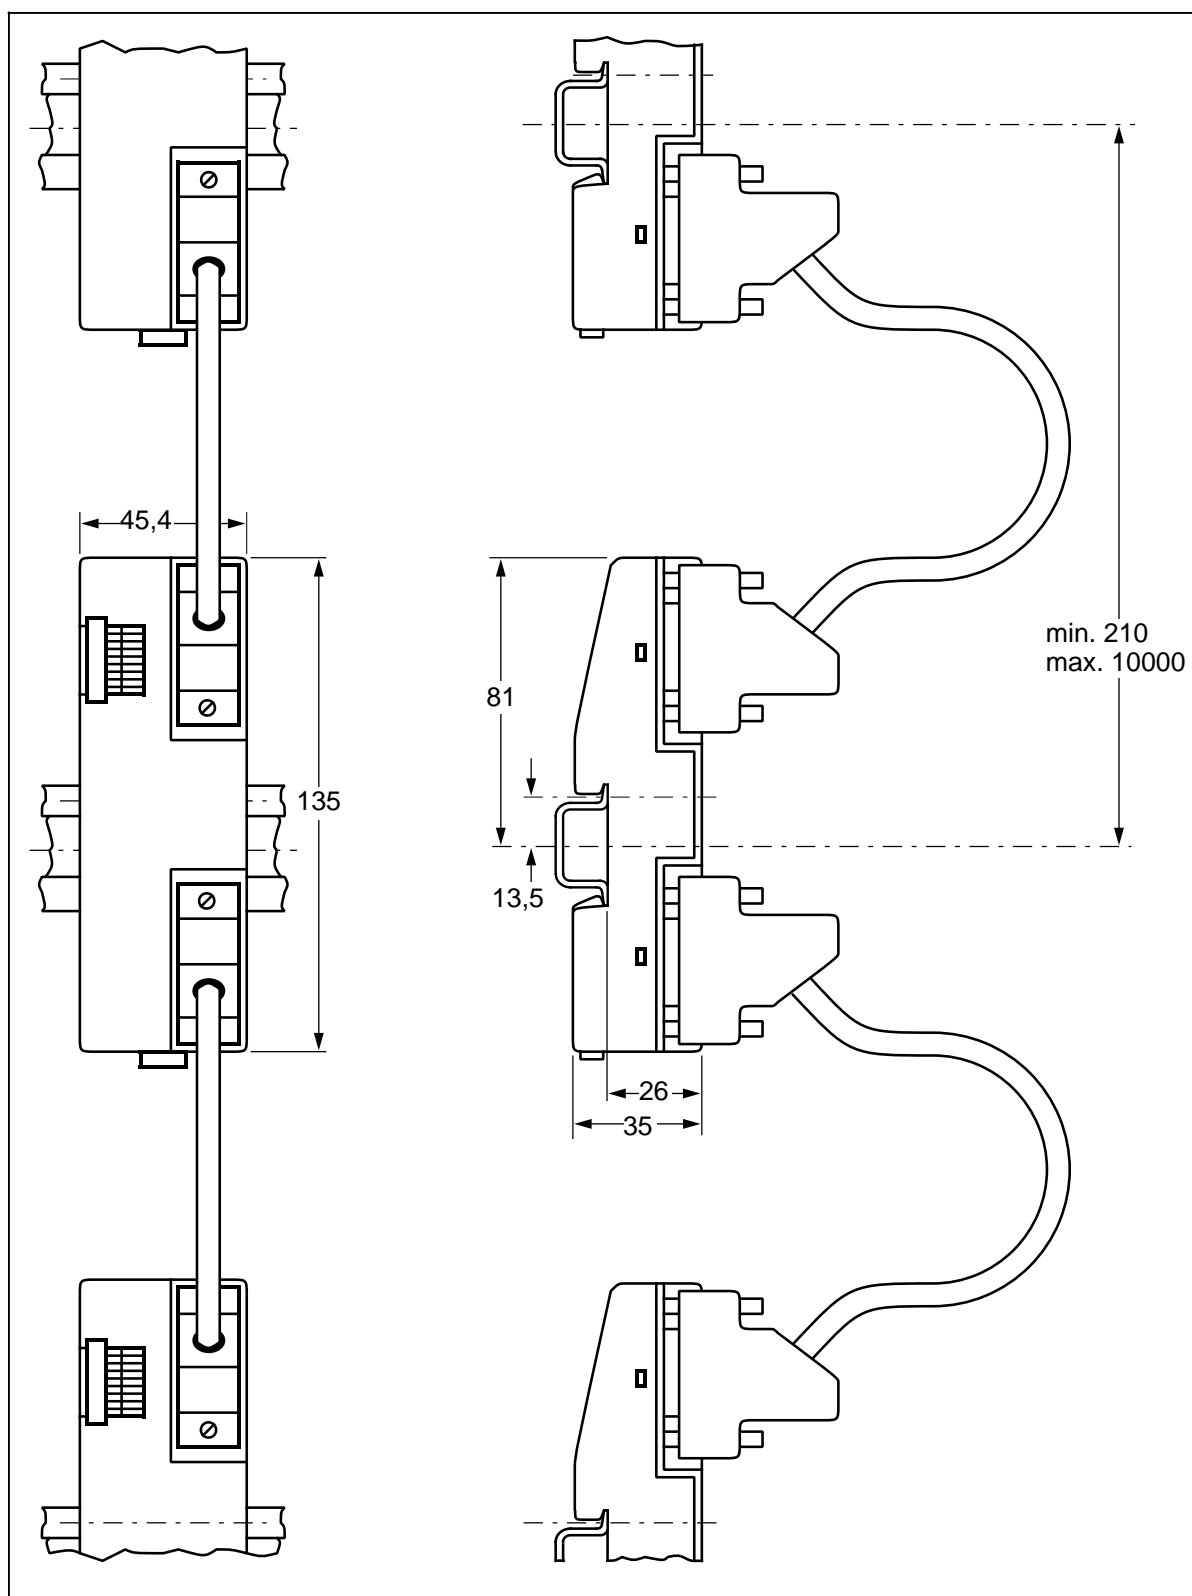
Maßbild der Anschaltungsbaugruppe IM 316 (6ES5 316-8MA12)
